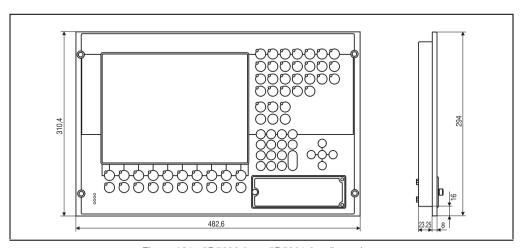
5D5600.0x et 5D5601.0x, dimensions
